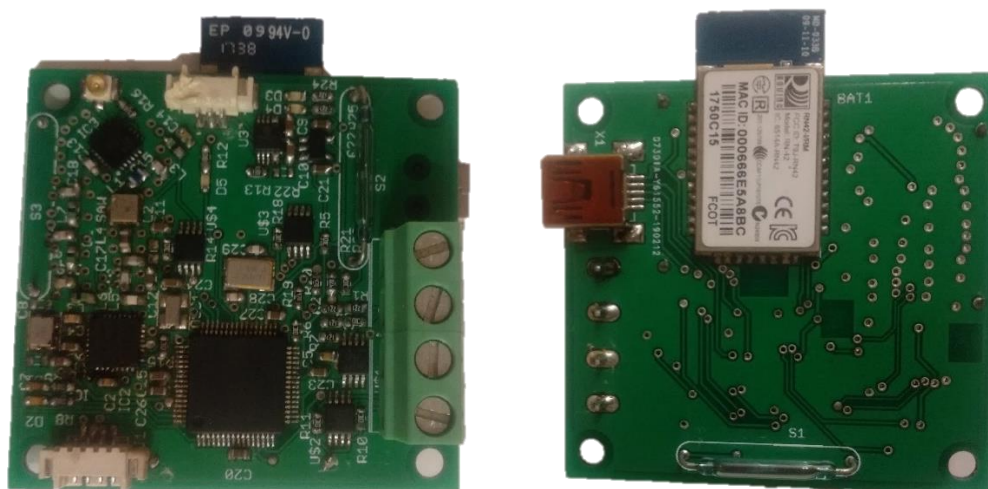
PCB ensamblada y soldada. fuente: elaboración propia.
